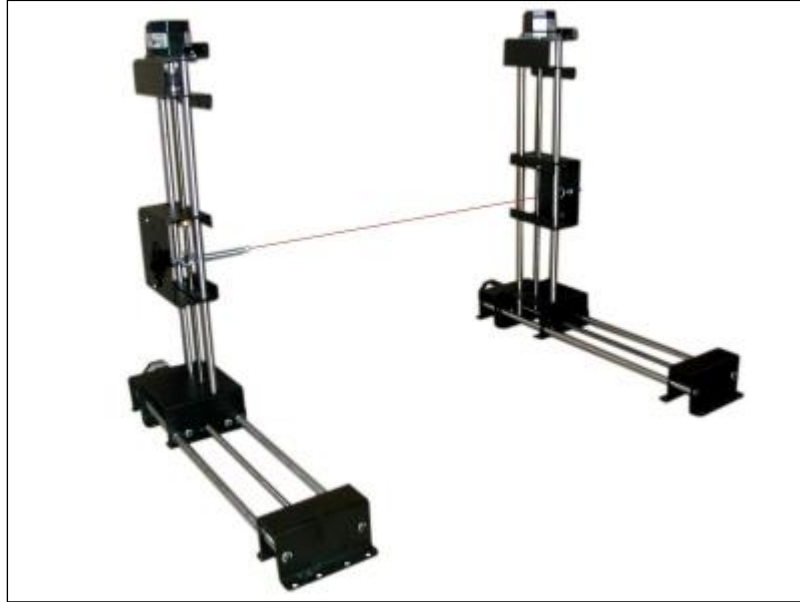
Máquina de corte de Poli estireno Expandido. Fuente [34]
